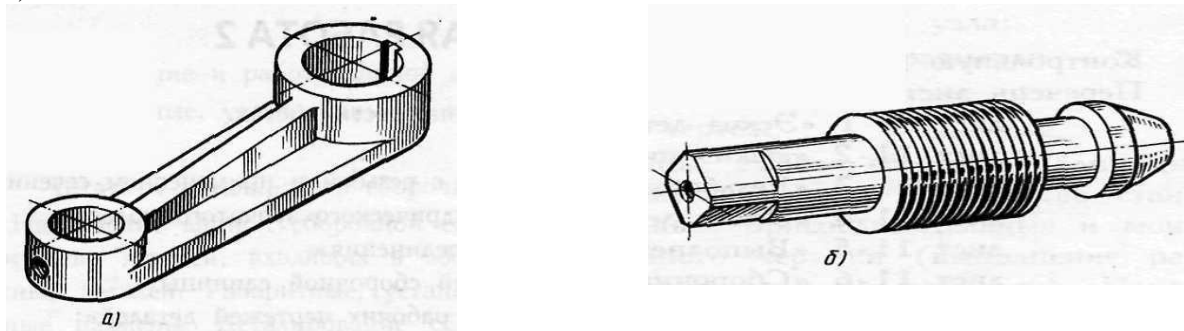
Примерные образцы деталей для эскиза к листу №5
